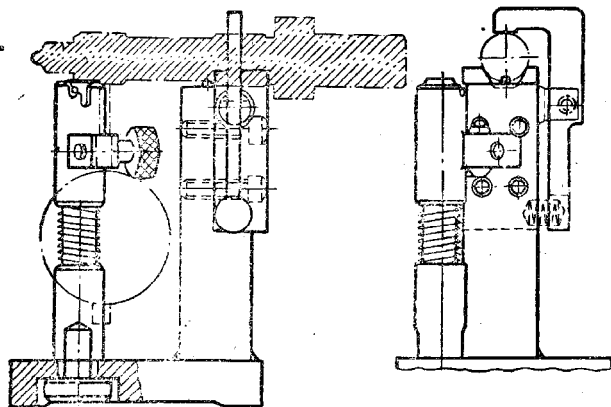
Приспособление ЛМ 9579-436 для проверки биения распылителя и муфты на собранной форсунке
